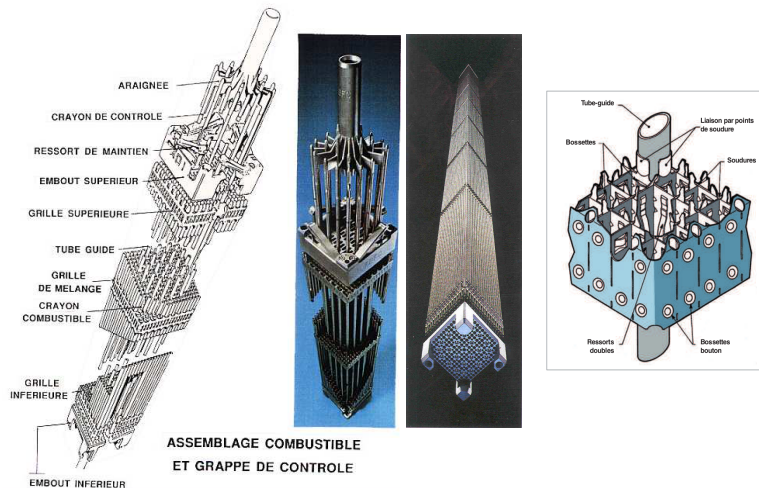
Un assemblage combustible REP. Schéma, vue de dessus et de dessous [BB02]
